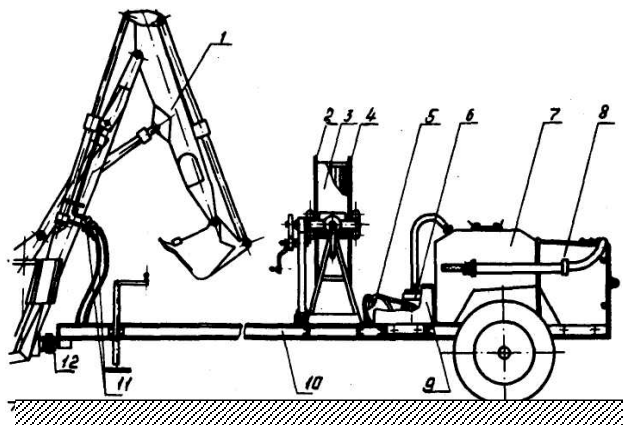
Ремонтный комплекс К-68А: 1 – экскаватор; 2 – барабан; 3 – шлаг; 4 – реактивная головка; 5 – привод насоса; 6 – насос; 7 – бак; 8 – насадка; 9 – капот; 10 – тележка; 11 – шланги гидросистемы; 12 – шарнир
